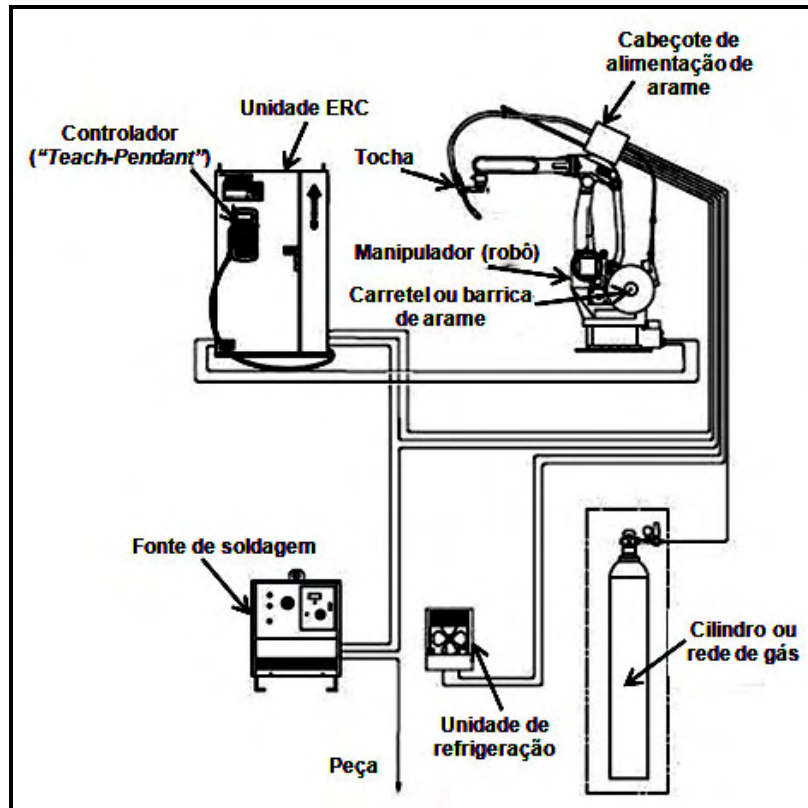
Desenho esquemático dos principais equipamentos utilizados no processo de soldagem GMAW robotizado (Adaptado de MOTOMAN, 1995).
